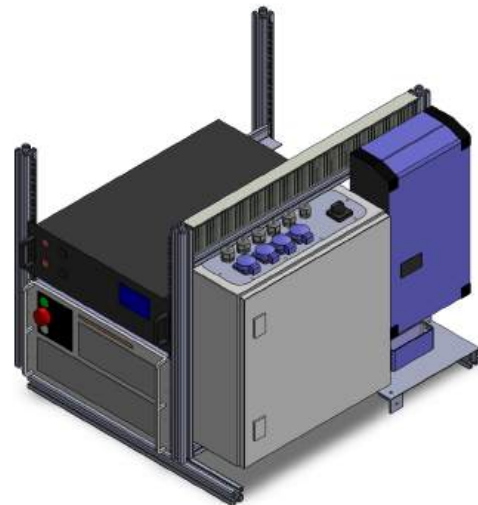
Verwendete Hauptkomponenten oberhalb des Werkzeugrahmens. Im Rack-Einschub auf der linken Seite im Bild sind die schwarze Batterie sowie das graue Lasergehäuse darunter abgebildet. Auf der rechten Seite ist der graue Schaltschrank sowie der blaue Wechselrichter/ Ladegerät zu erkennen.
